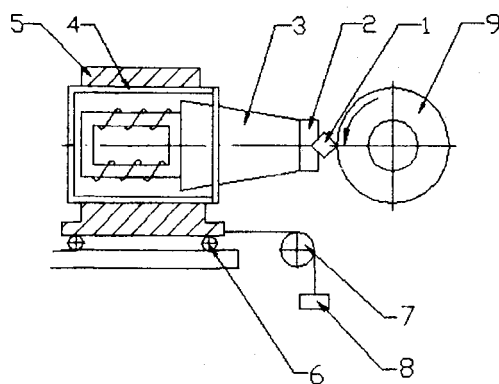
Схема механического распиливания при сообщении заготовке ультразвуковых колебаний
